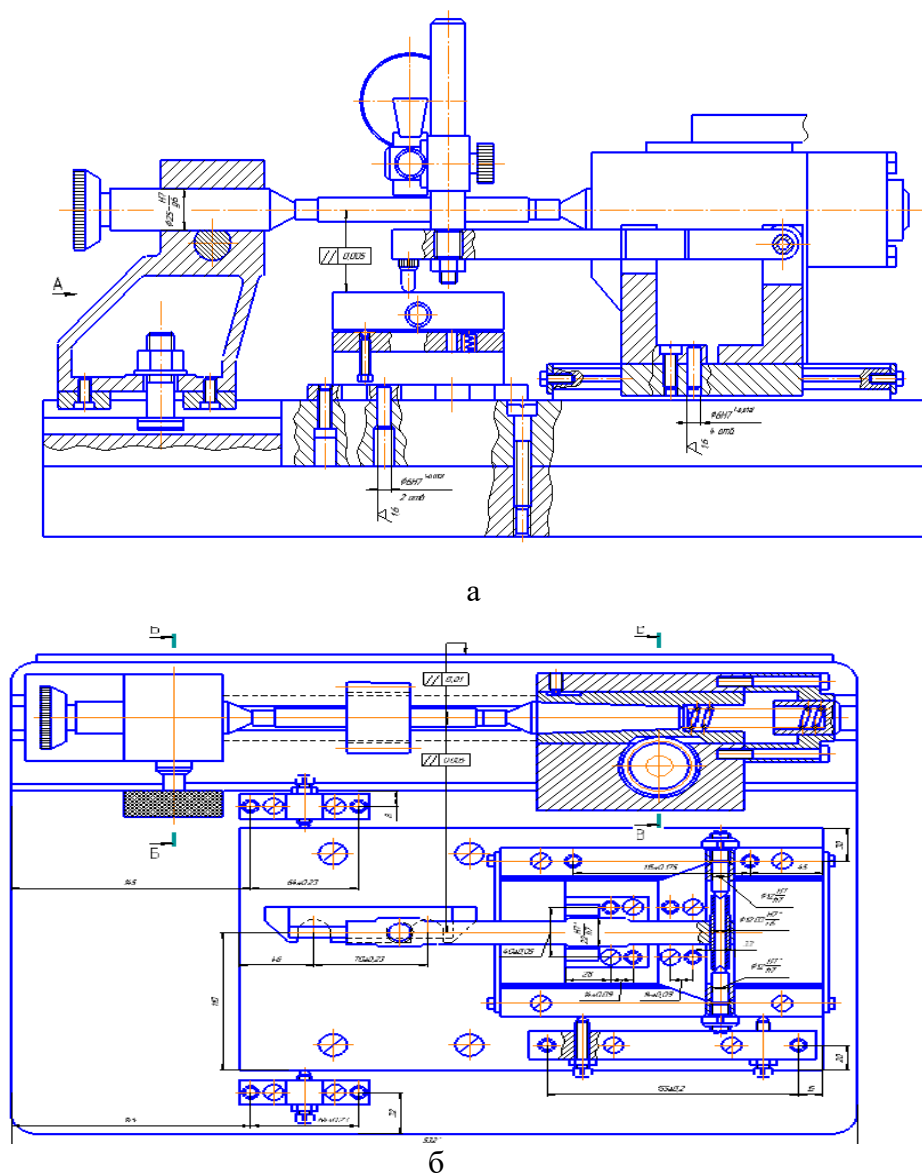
Контрольне пристосування для контролю похибки направлення зубів шестерні
